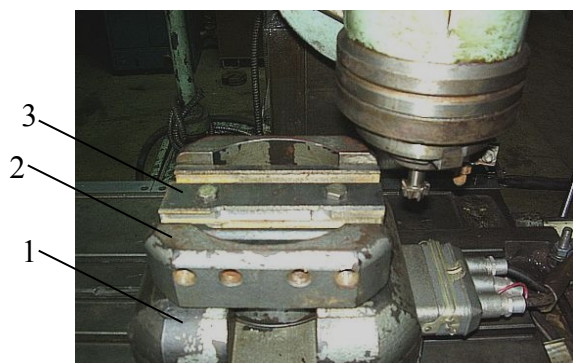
Измерительное устройство (1 – УДМ 600; 2 – столик; 3 - заготовка)
